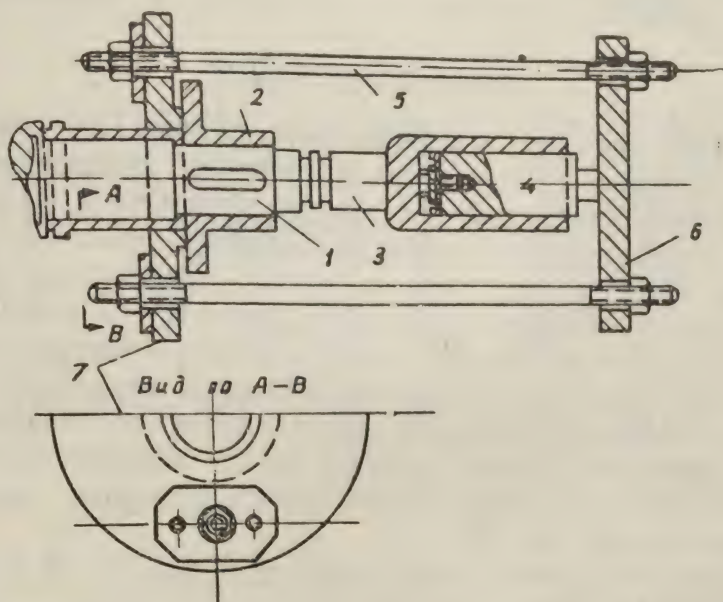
Конструкция приспособления для снятия деталей с валов:
